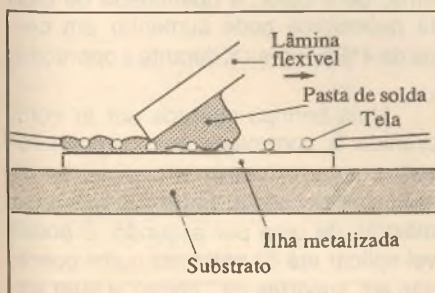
Aplicação de pasta de solda por impressão com tela.
